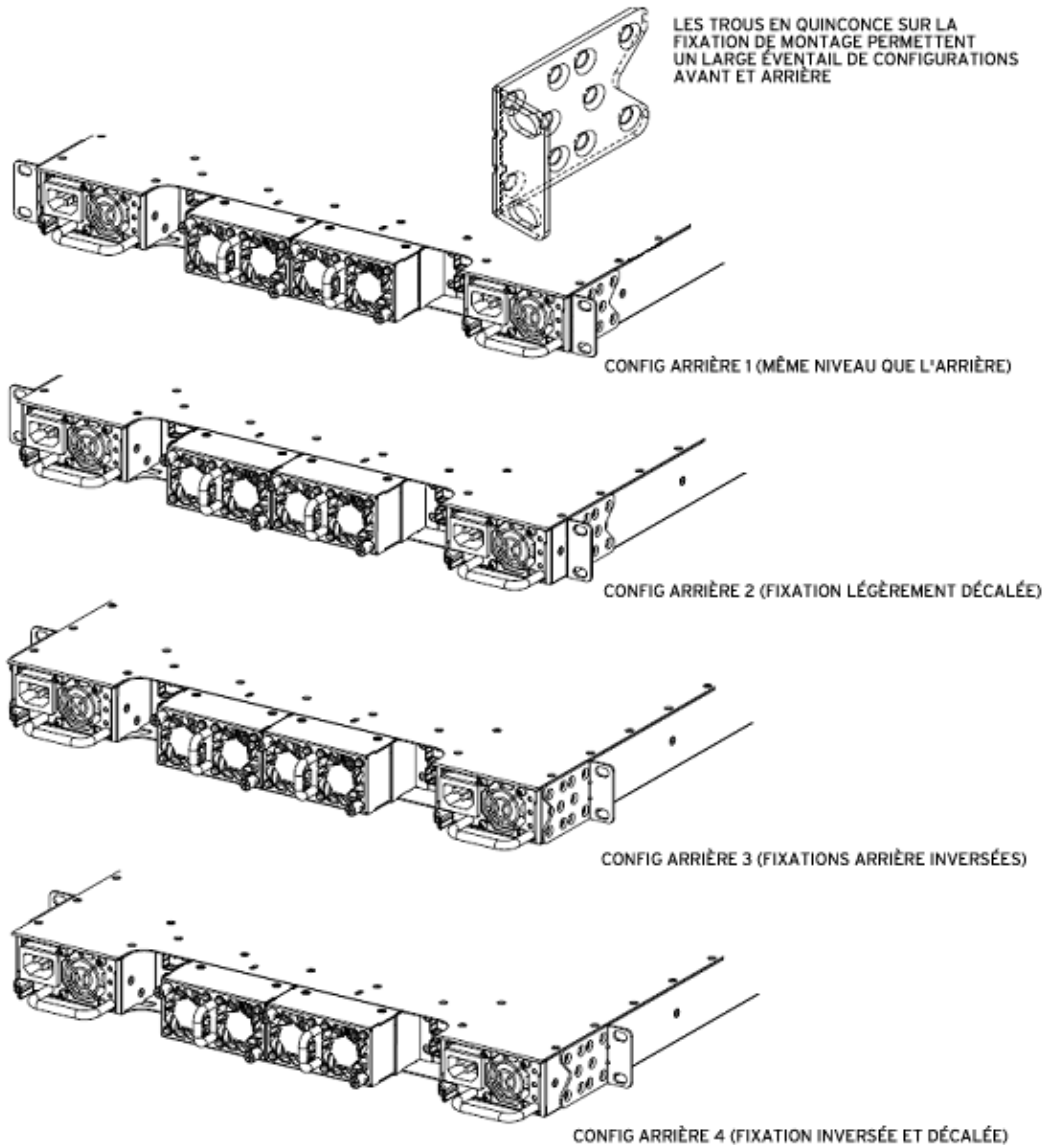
Options d'installation de la fixation de montage arrière sur boîtier
